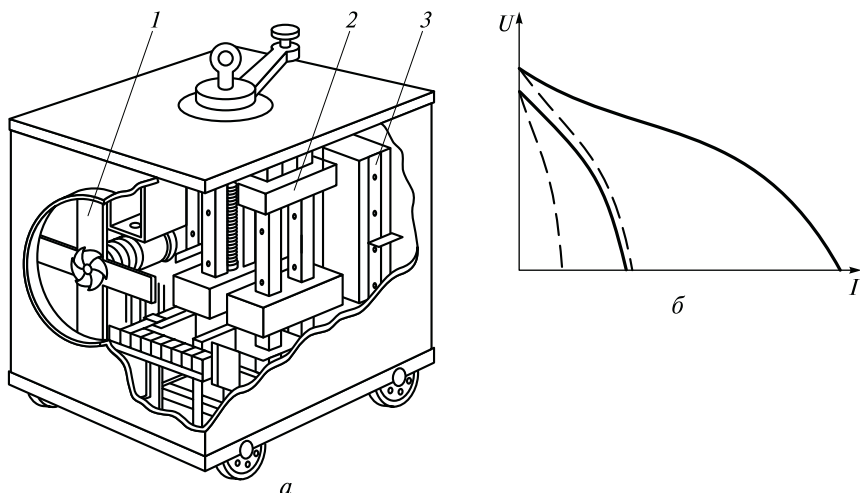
Сварочный выпрямитель ВД-306УЗ:
